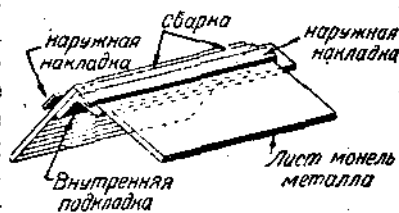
Сварка листов монель-металла толщиной свыше 1,5 мм.
